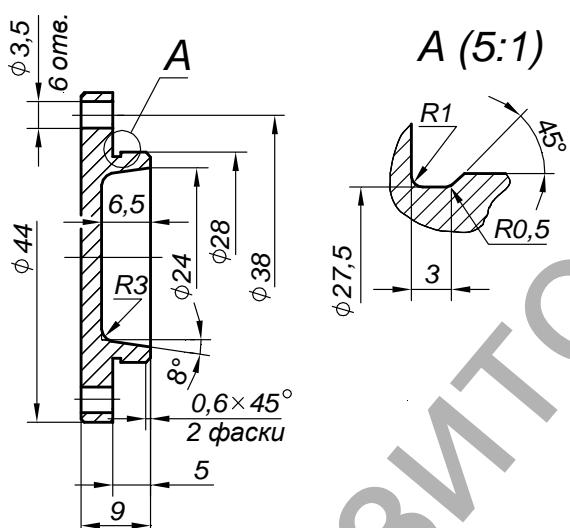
Учебный рабочий чертеж крышки, учитывающий все особенности её конструкции (без упрощений)
